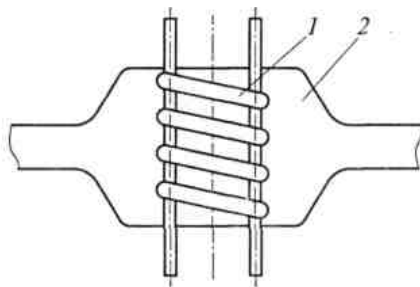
Внутренний спиральный сваривающийся холодильник: 1 — холодильник; 2 — полость формы для массивной части отливки
